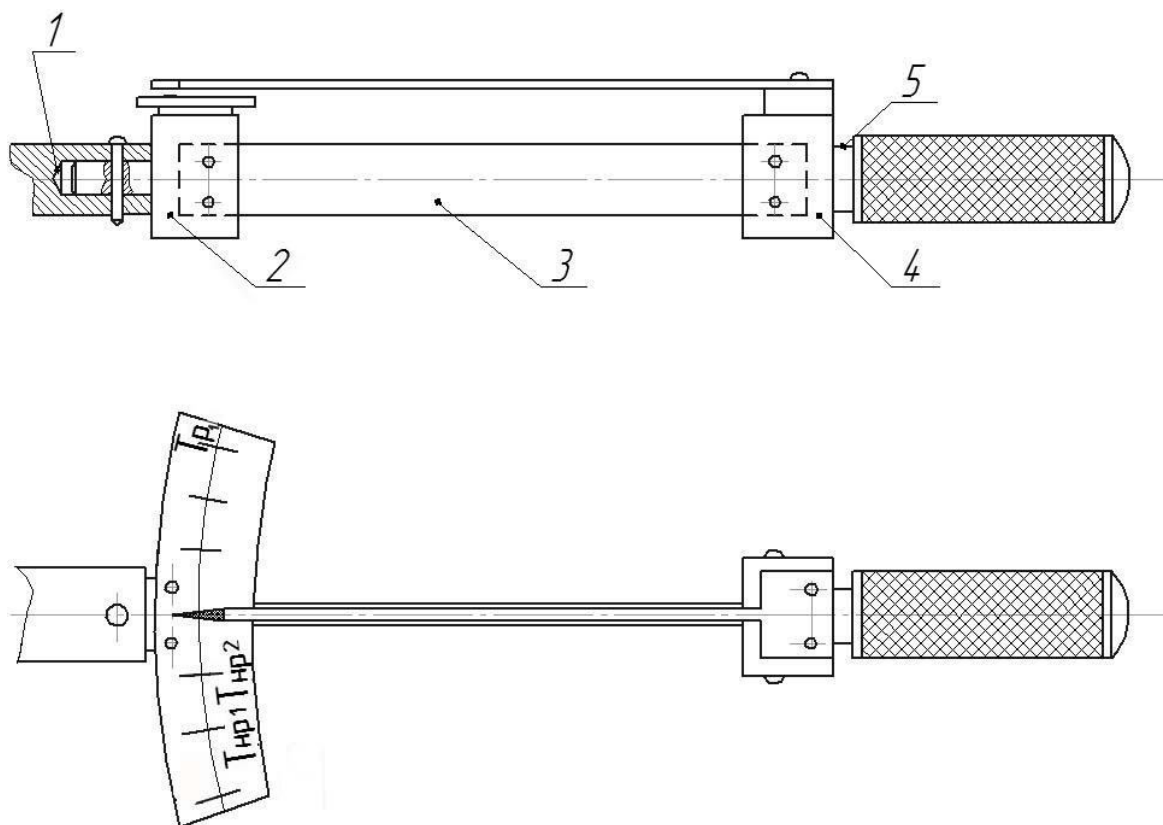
Схема динамометрического ключа контроля натяжения ленты: 1 - рукоятка механизма натяжения; 2 – вилка передняя с цилиндрическим концом и шкалой; 3 - упругая пластина; 4 – вилка задняя с ручкой и стрелкой; 5 – канавка для подвески тарировочных грузов.
